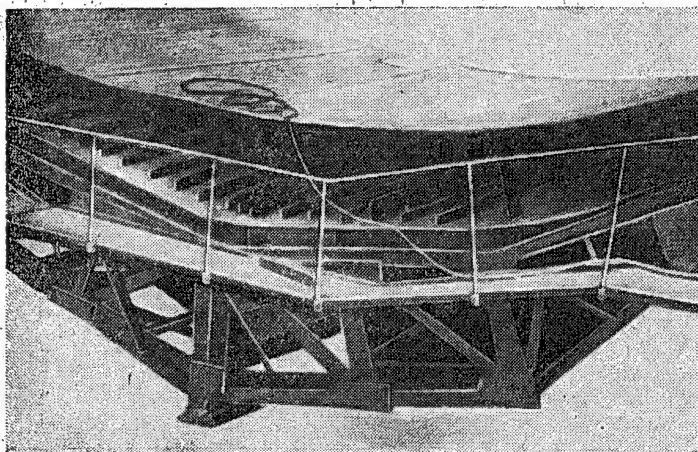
Поворотная постель для сборки и сварки днищевой секции судна
